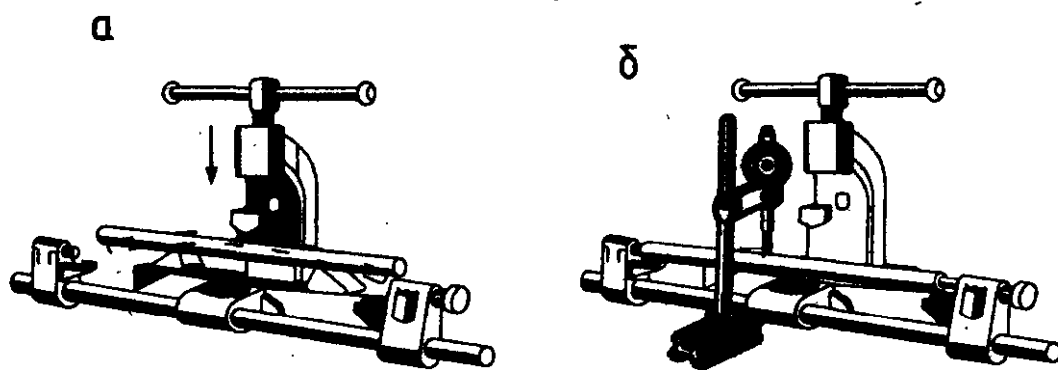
Правка вала на ручном прессе (а) и проверка изгиба индикатором (б)
